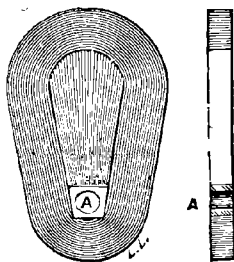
Bobine séparée de l'alternateur Ferranti.
